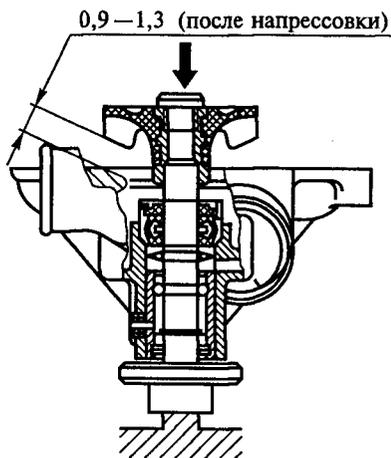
Напрессовка крыльчатки водяного насоса
